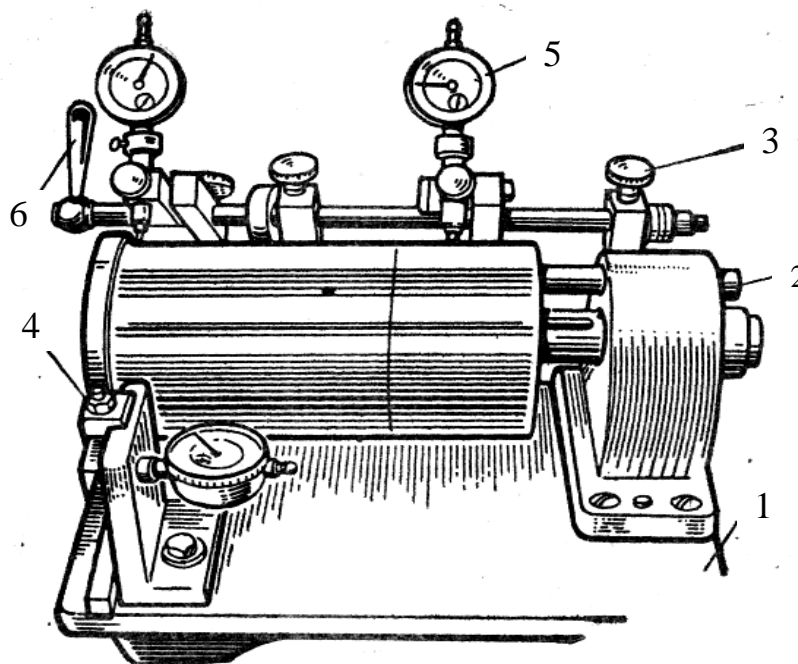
Приспособление для проверки биения опорного торца бурта и посадочных поясов относительно внутренней поверхности КИ-3340 ГОСНИТИ: 1 – плита; 2, 3 – стойки; 4 – упор; 5 – индикатор; 6 – рукоятка
